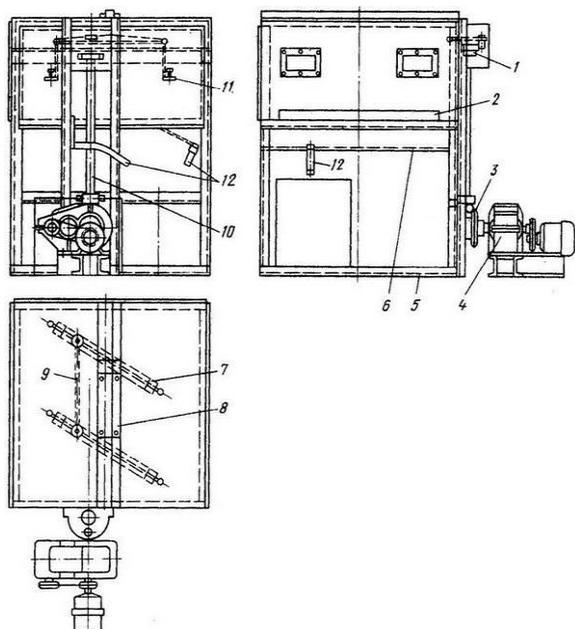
Глазуровочная камера: 1 – шатунно-кривошипный узел; 2 – щели; 3 – коническая пара шестерен; 4 – редуктор; 5 – станина; 6 – корыто; 7 – рычаг; 8 – планка крепления корпуса; 9 – соединительная тяга; 10 – вертикальный вал; 11 – пульверизатор; 12 – слив глазури в бак
